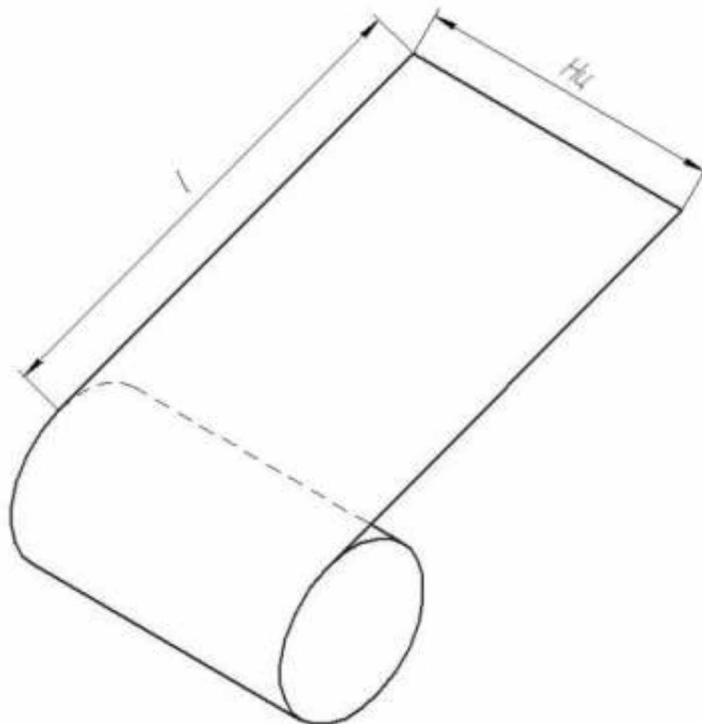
Схема розгортання оброблюваної циліндричної поверхні
